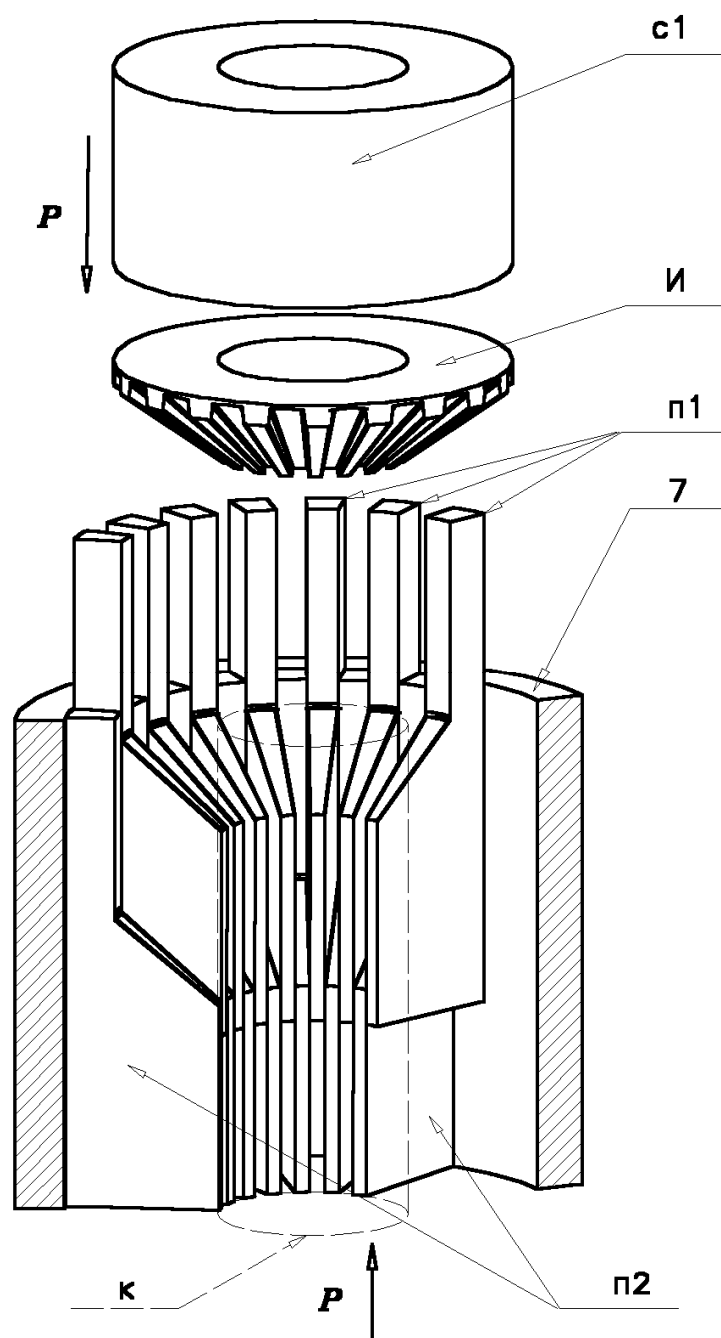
Пресс-форма для формования изделия в виде шестерни конической зубчатой передачи
